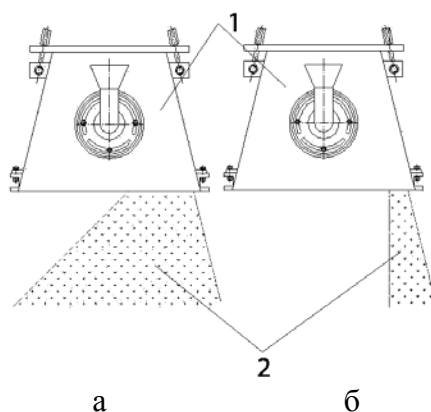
Различные потоки дробы при использовании обычных дробеметных колес и колес с магнитной регулировкой вылета дробы:
